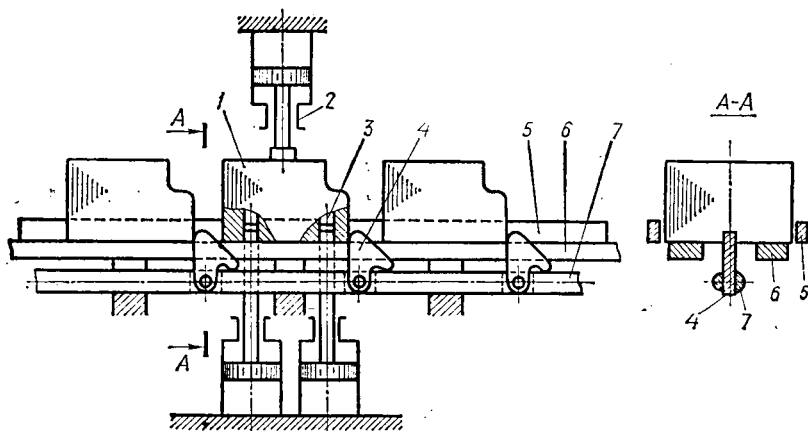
Схема устройства для перемещения заготовки или приспособления спутника
